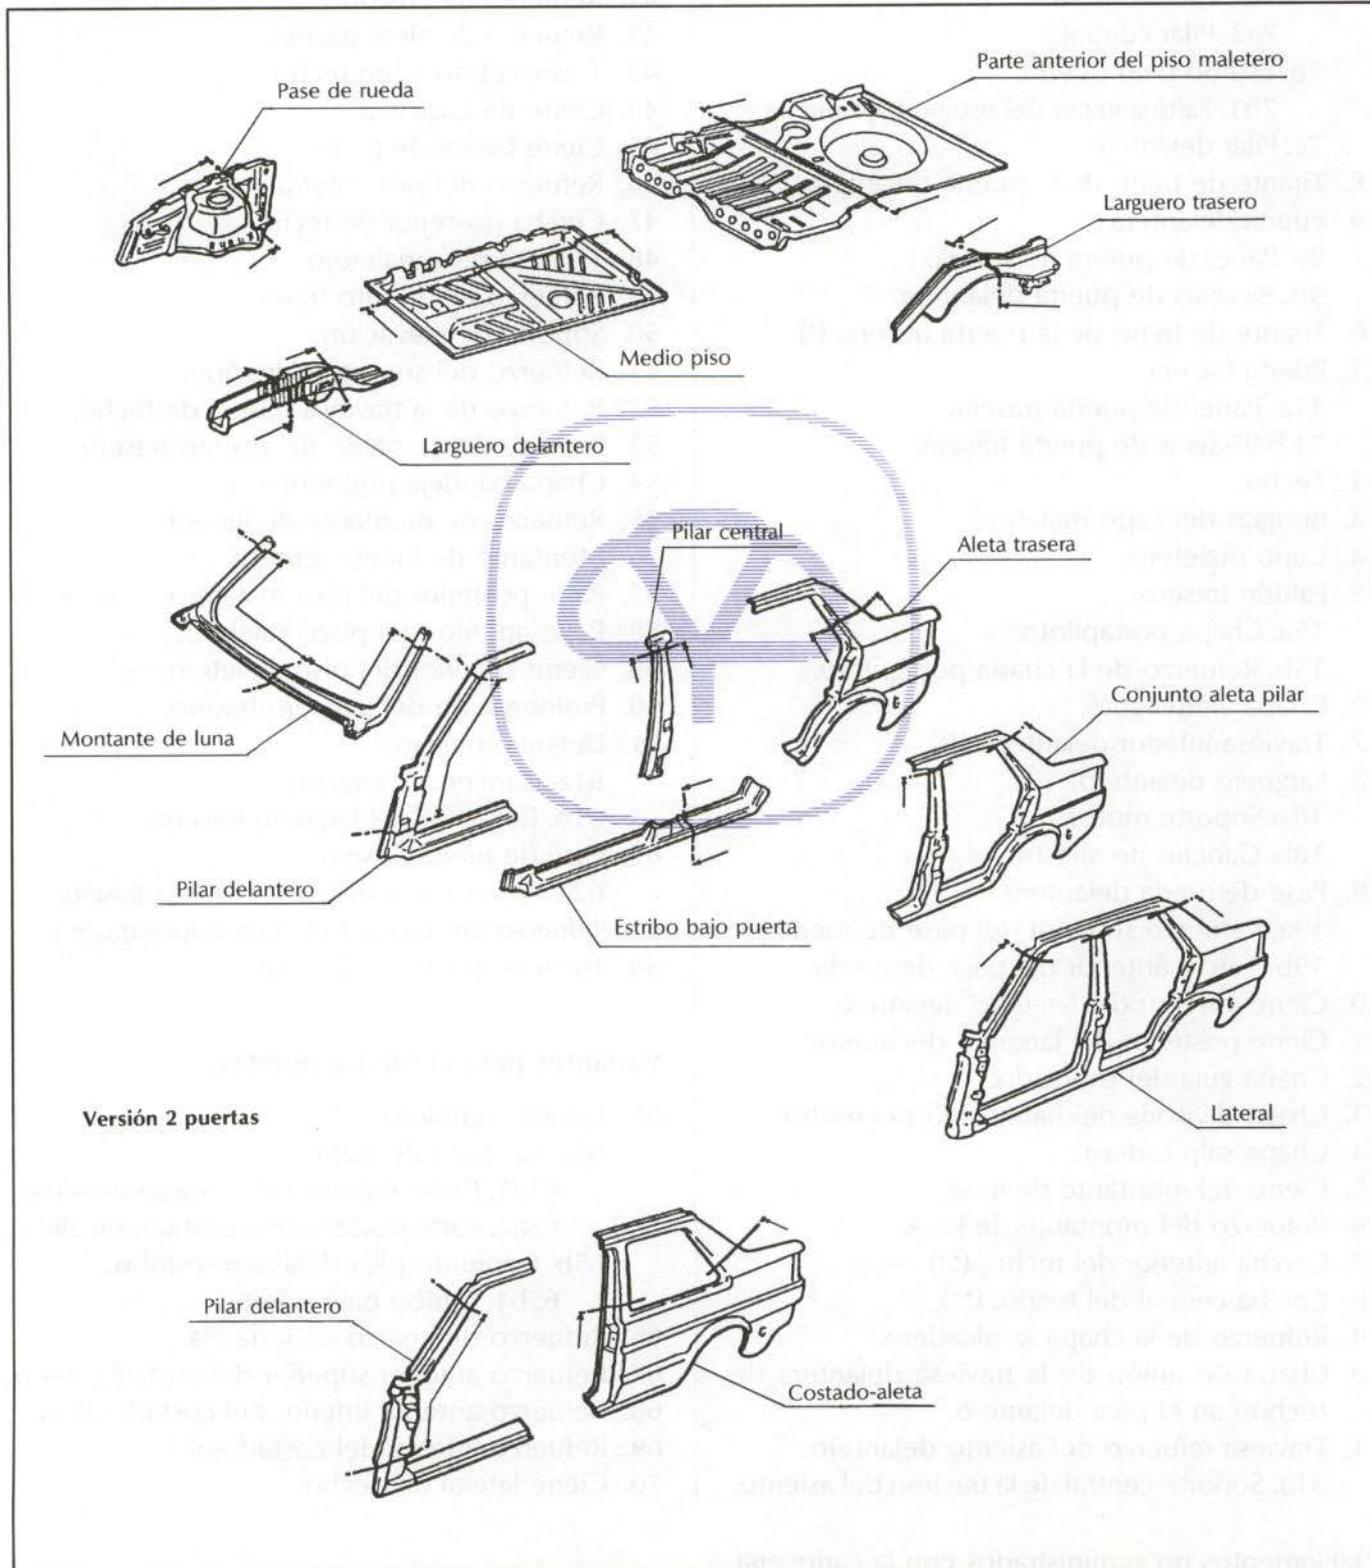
Secciones de ahorro contempladas por el fabricante.
